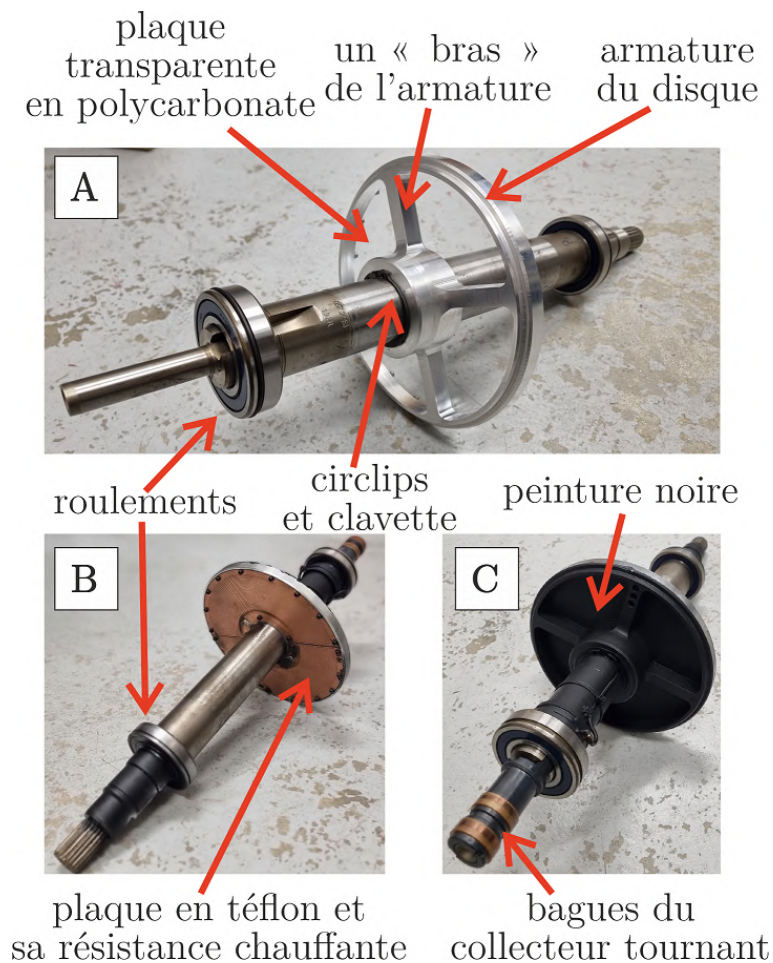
Photographies des rotors utilisés sur le banc 2 - A) vue arrière du rotor à disque transparent ; B) vue avant du rotor « mesures thermiques » ; C) vue arrière du rotor « mesures thermiques »
